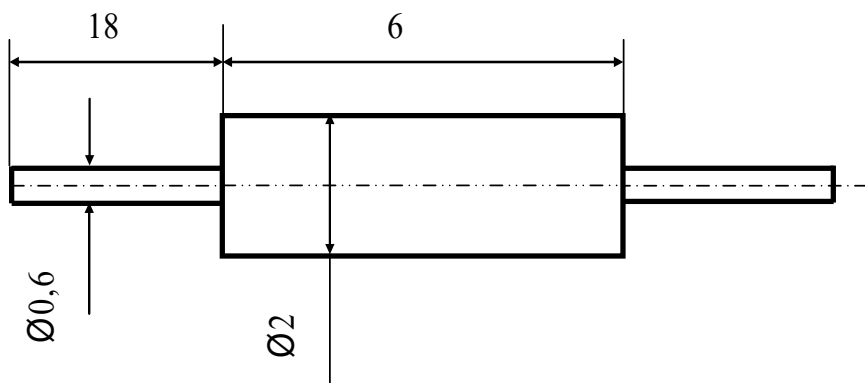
Внешний вид резистора МЛТ-0,125
